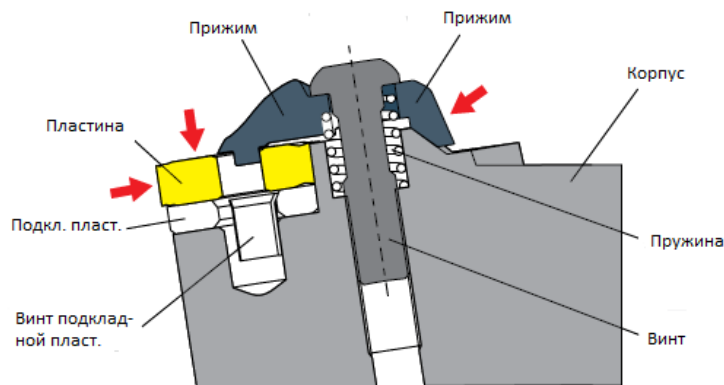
Державка для резца DCLNR/L-2020K12.
